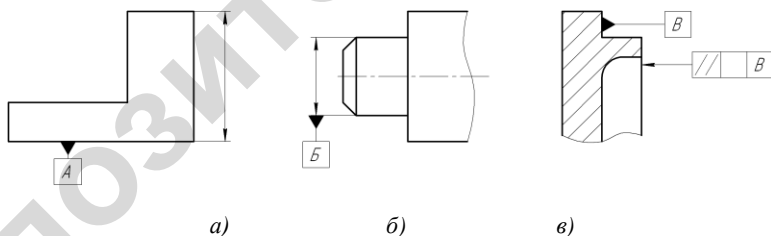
Правила нанесения условных обозначений баз на чертежах деталей
